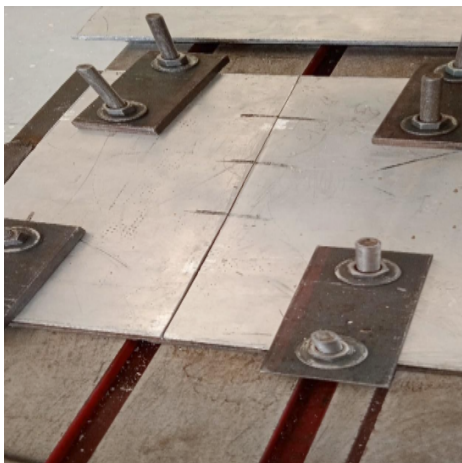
Пластины, закрепленные на столе вертикально-фрезерного станка
